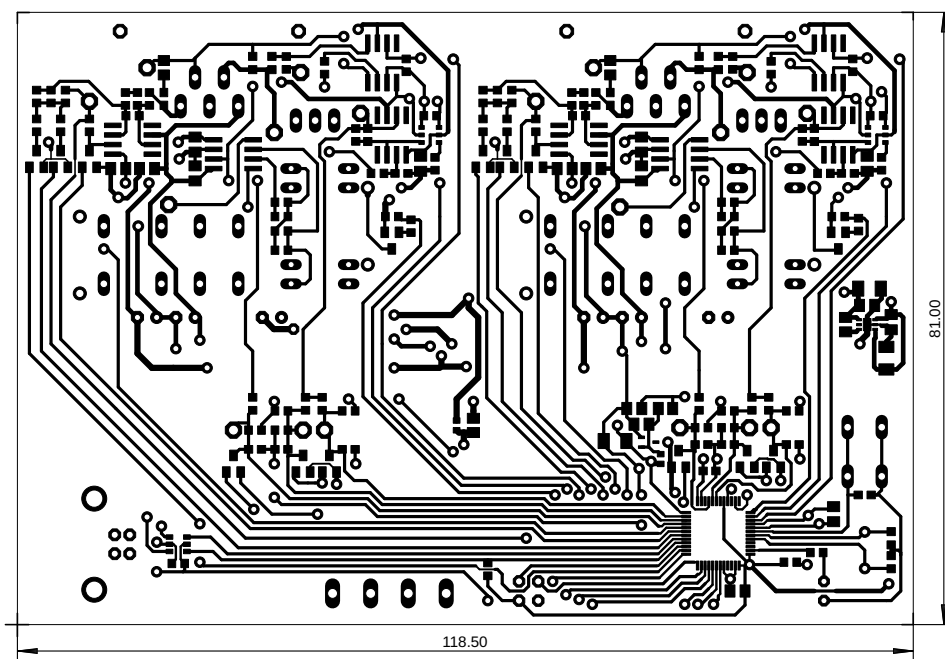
Fotografie - Pohled ze spodní strany spojů
